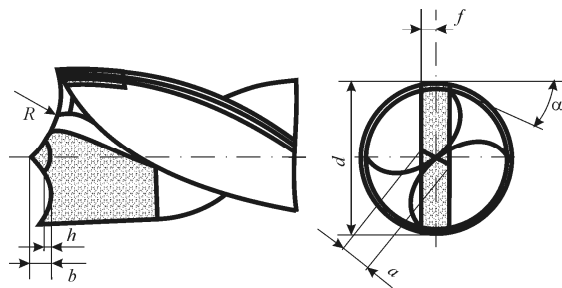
Спиральное сверло с подрезающей режущей кромкой [4]
